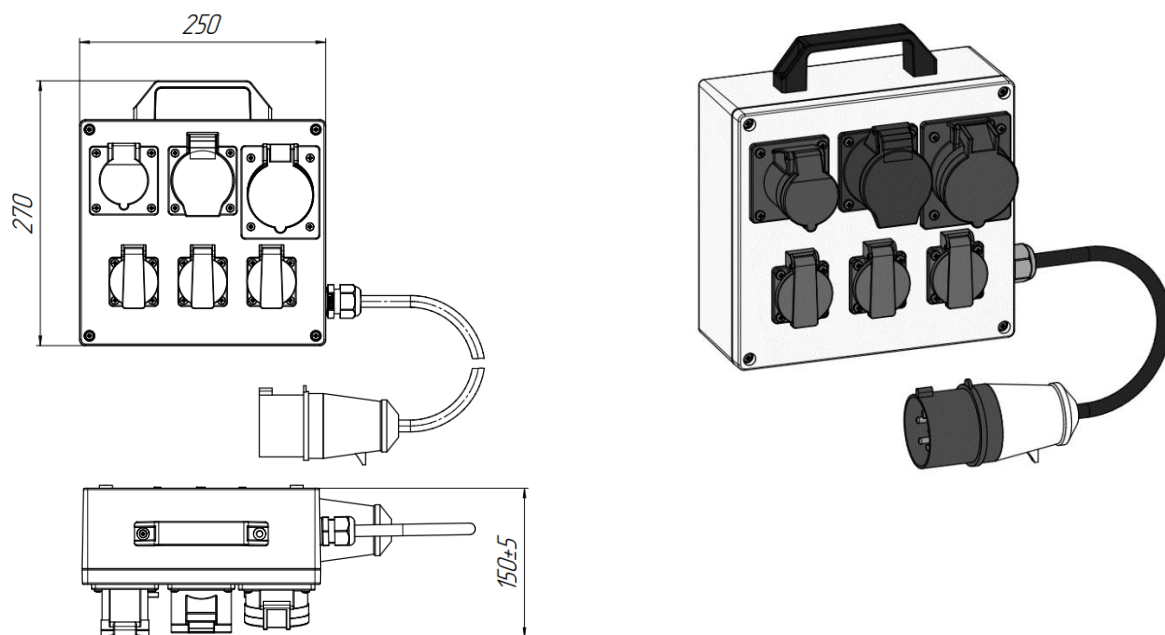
Габаритные размеры и внешний вид распределителя (А), с фронтальным расположением розеток
